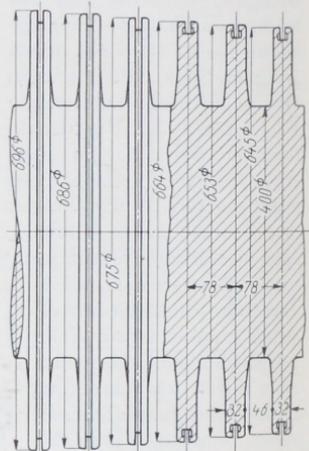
Mit der Welle aus einem Stück gedrehter Läufer, AEG, Berlin. M. 1:10.
